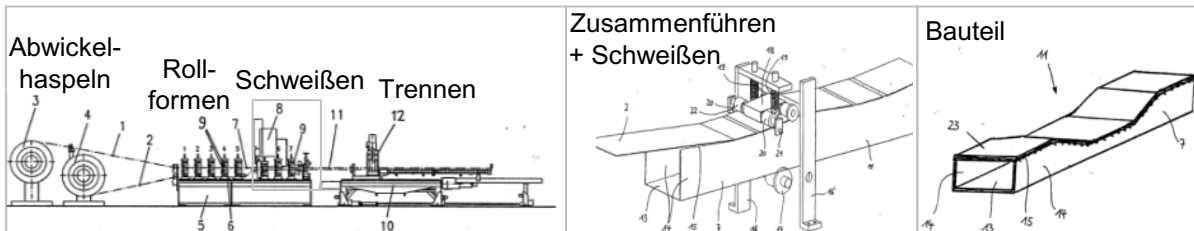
Dreistern-Technologie zum Fügen eines Profils und Blechs zu einem Hohlprofil mit veränderlichem Querschnitt; Prozesskette (links), Schweißeinheit (mittig), Zielbauteil (rechts); in Anlehnung an Patentschrift EP 1 371 430 A2 [DRE03]
